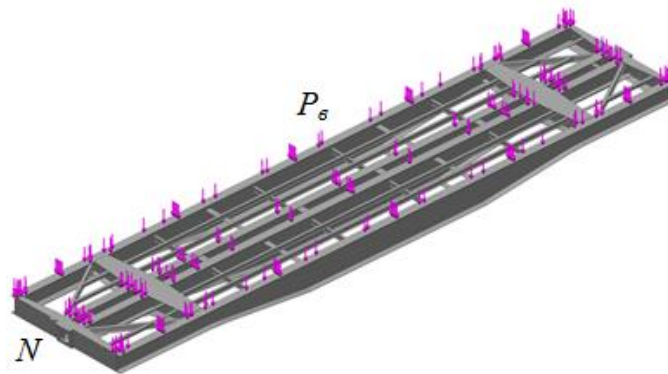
Розрахункова схема несучої конструкції вагона-платформи при I розрахунковому режимі
